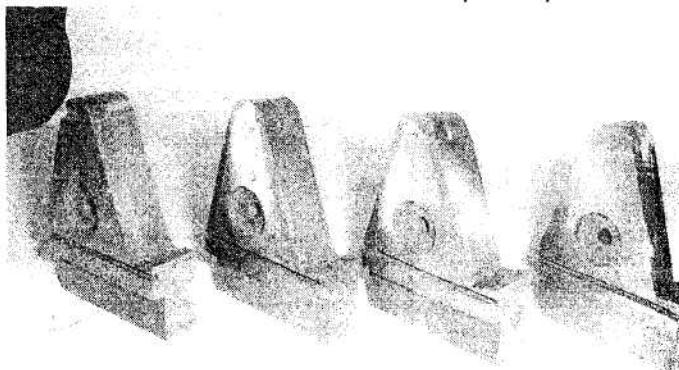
Зношені зуби черв'ячної твердосплавної фрези
